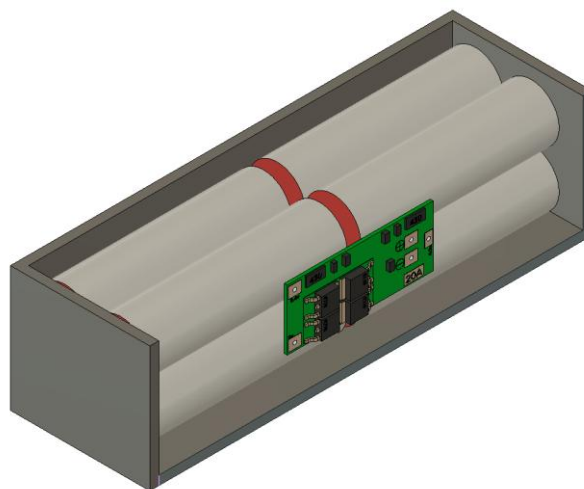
Формування батарейного відсіку корпусу пристрою
